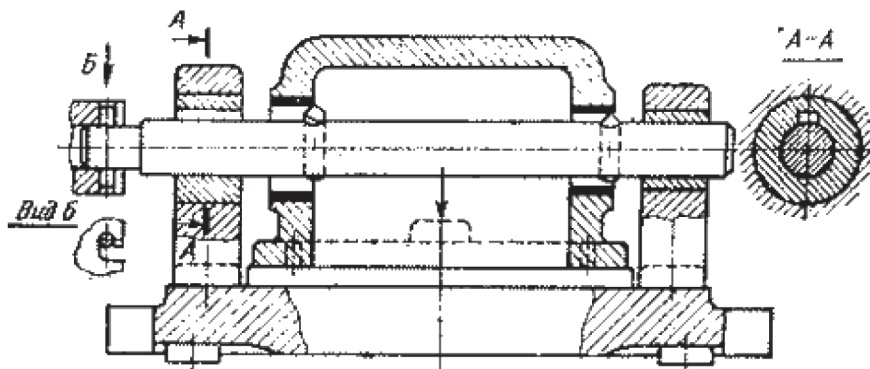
Направляюча втулка для борштанги (схема розточувального пристрою)
